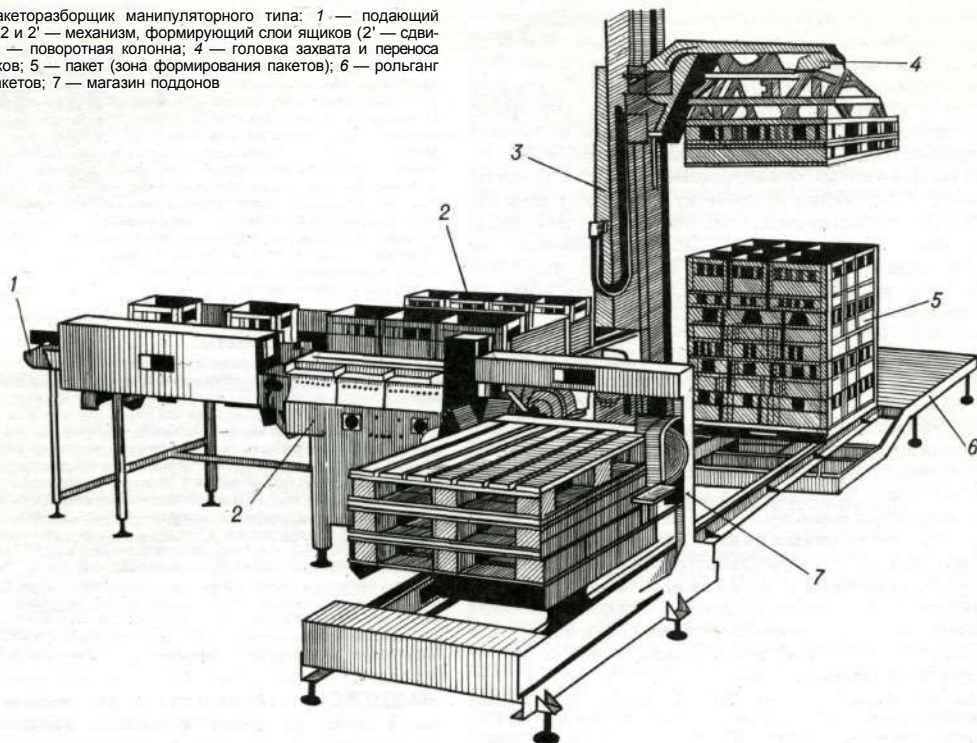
Пакеторазборщик манипуляторного типа: 1 — подающий ролик; 2 и 2' — механизм, формирующий слои ящиков (2' — сдвигатель); 3 — поворотная колонна; 4 — головка захвата и переноса слоя ящиков; 5 — пакет (зона формирования пакетов); 6 — ролик выдачи пакетов; 7 — магазин поддонов
